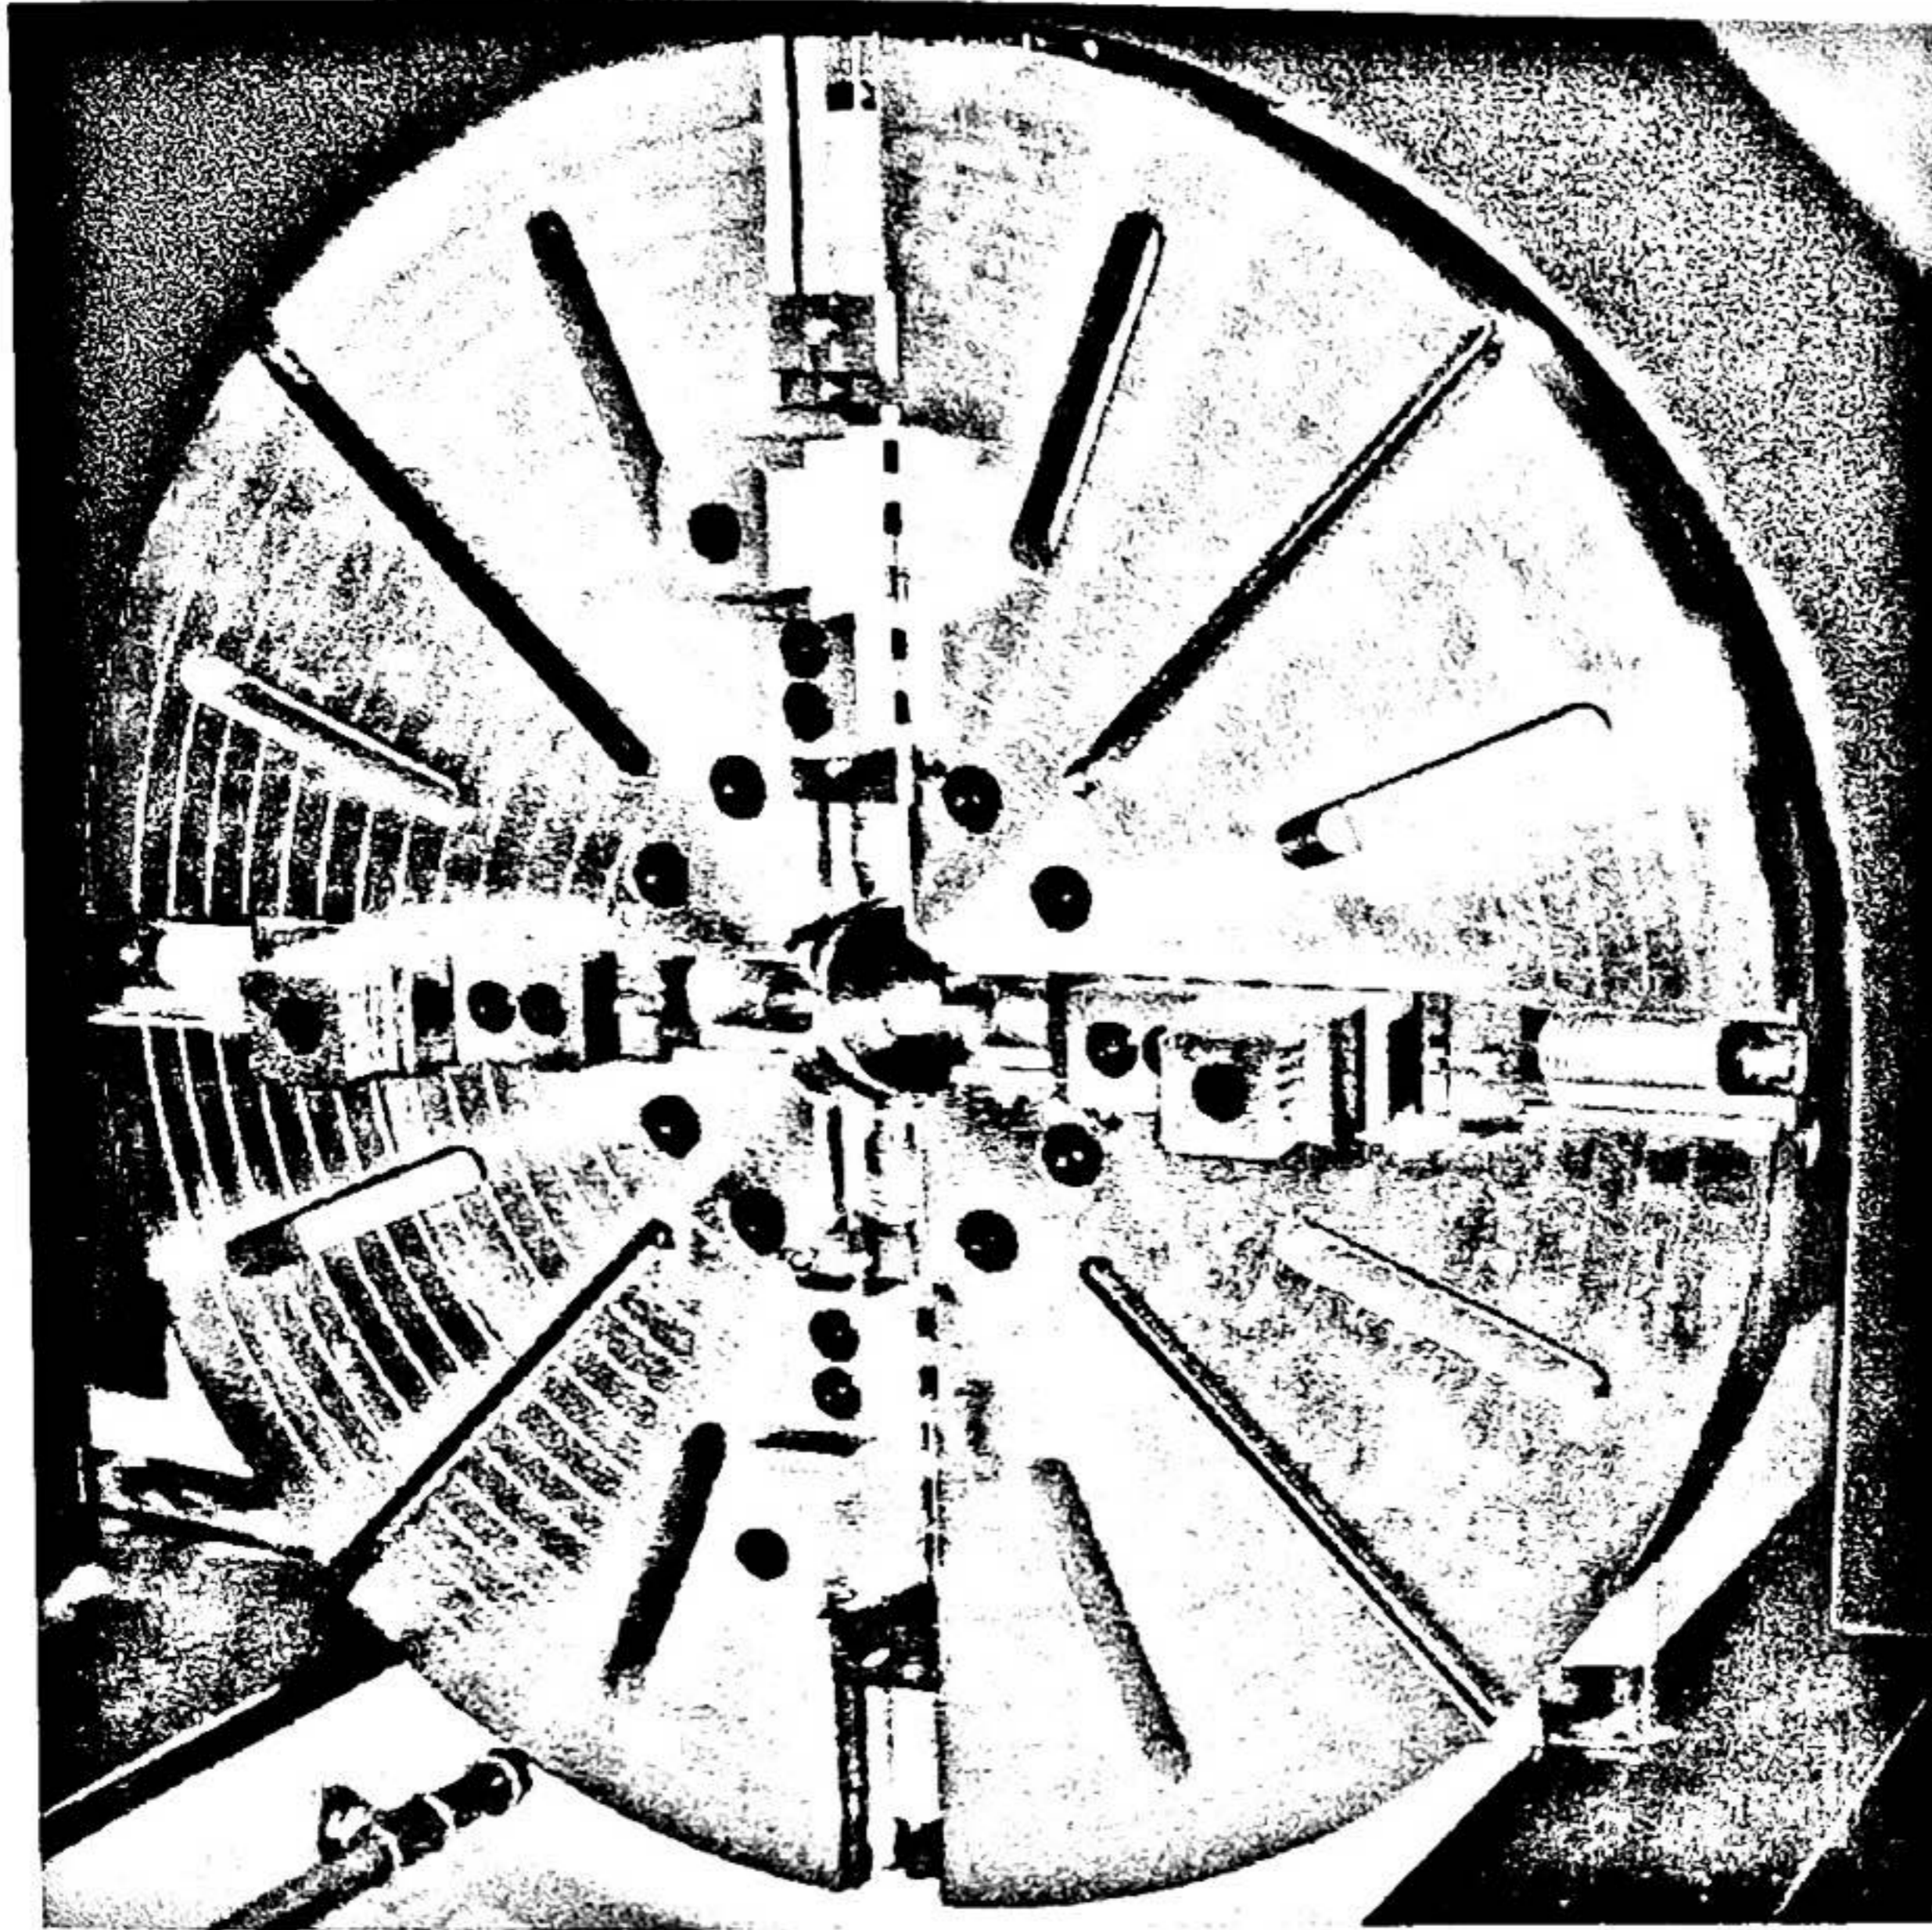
/3: Vorderseite Spindelkasten mit Schutzhaube, Spindel, Planscheibe mit vier Backen
